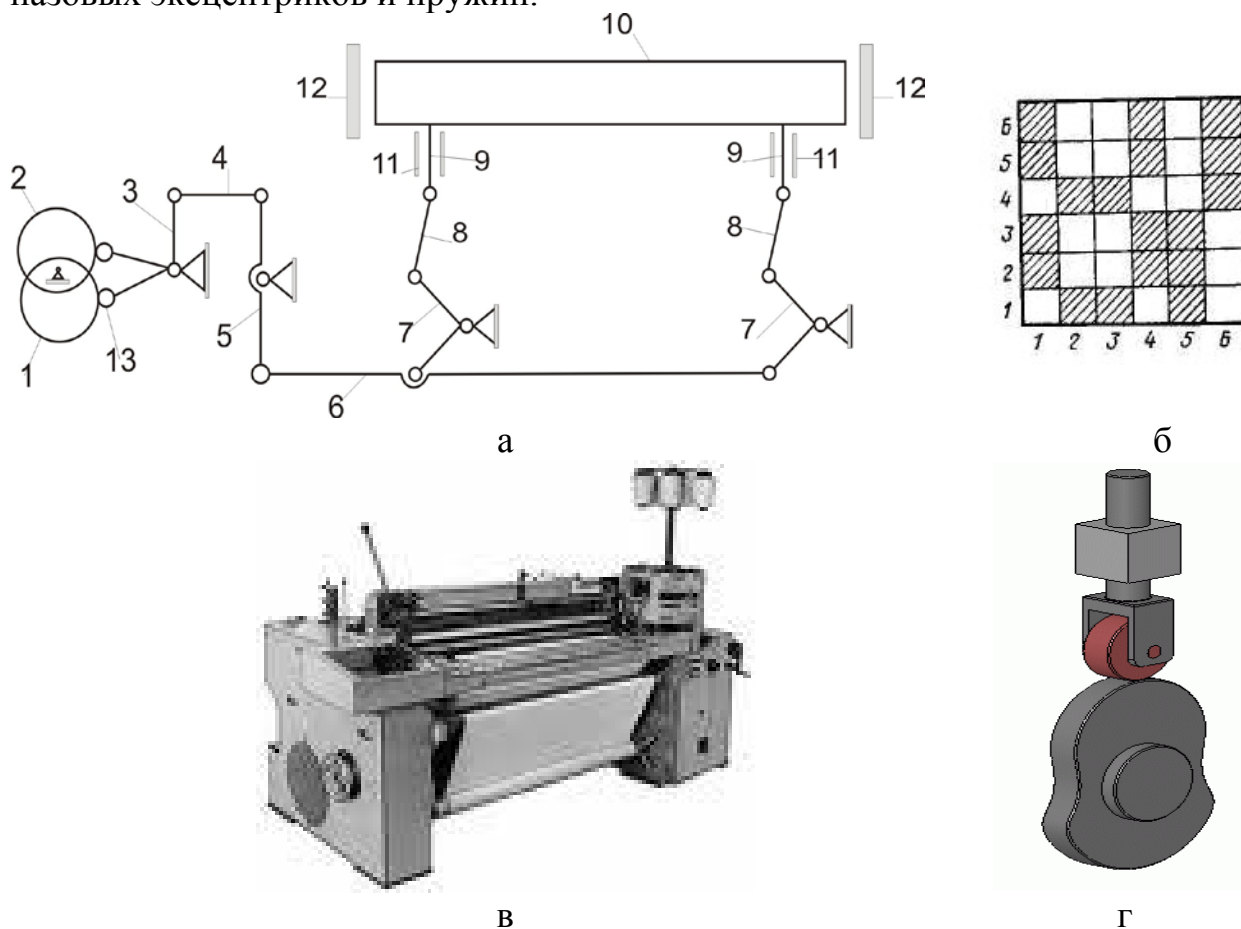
а) схема кулачкового зевобразовательного механизма станка СТБ; б) рисунок переплетения для подбора кулачков; в) внешний вид ткацкого станка СТБ с кулачковым зевобразовательным механизмом; г) кулачок с роликом
